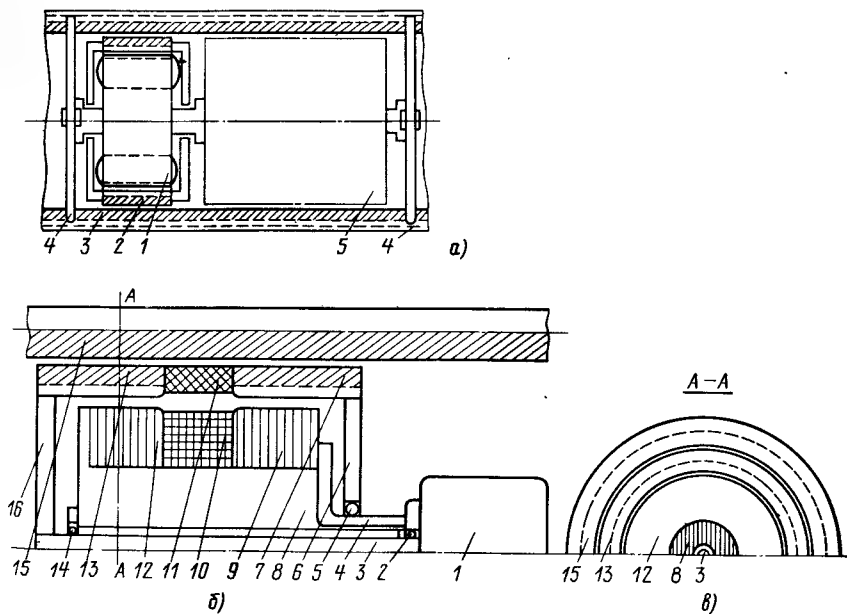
Привод поступательного движения с промежуточным ротором: а — из постоянных магнитов; б, в — с ферромагнитным промежуточным ротором
